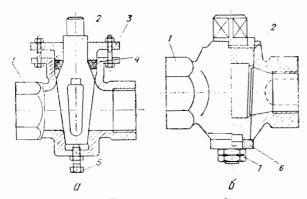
Пробковые краны муфтовые: а — сальниковый; б — натяжной; І — корпус; 2 — пробка; 3 — крыяка сальника; І — сальниковая пабняка: 5 — ограничительный болт; 6 — шайба; 7 — натяжная гайка.
